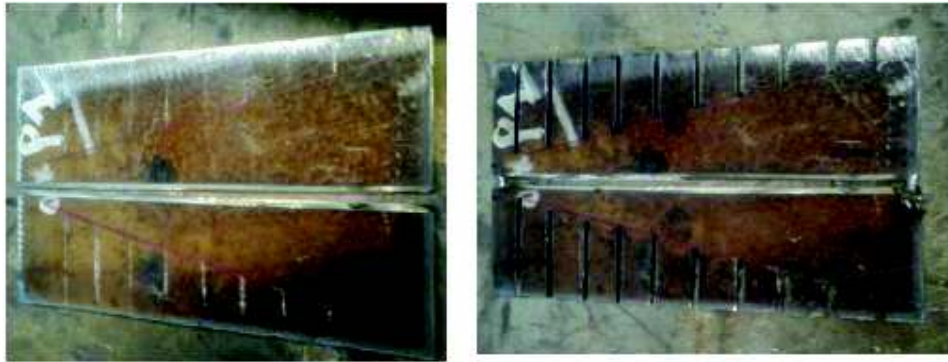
Diseño de ranuras en placa para ensayo Houldcroft.
